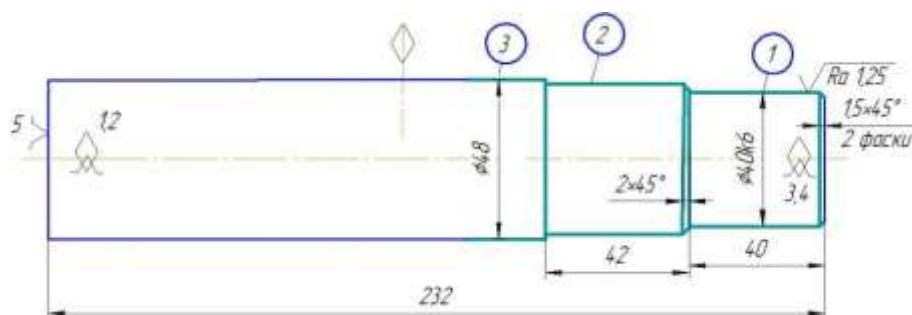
Обробка поверхні $\varnothing 40$
